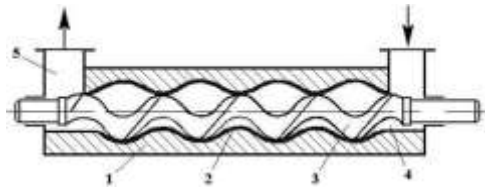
Схема одногвинтового (героторного) насоса: 1 – корпус; 2 – циліндр; 3 – гвинт; 4 – всмоктувальна порожнина; 5 – напірний трубопровід
